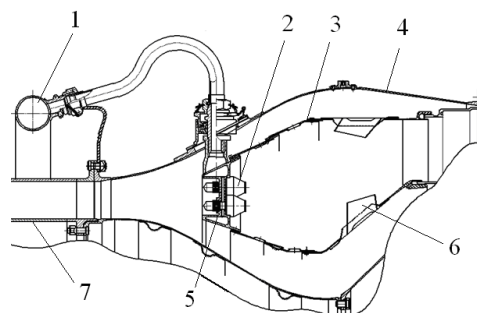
Конструктивная схема камеры сгорания: 1 – газовый коллектор, 2 – верхний, нижний ярус форсунок, 3 – жаровая труба, 4 – корпус камеры, 5 – корпус головки, 6 – патрубki, 7 – проставка
